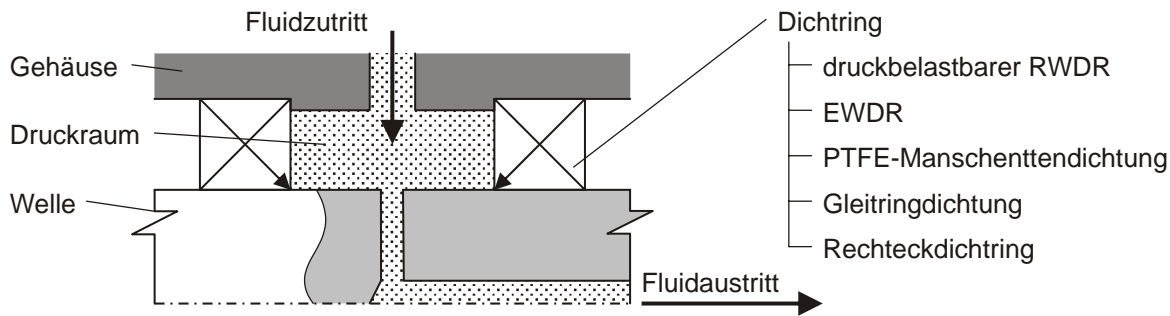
Grundaufbau einer radialen Drehdurchführung
